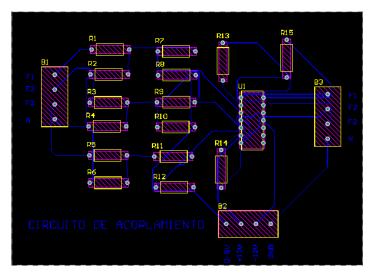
Diseño de la PCB del circuito de acoplamiento
